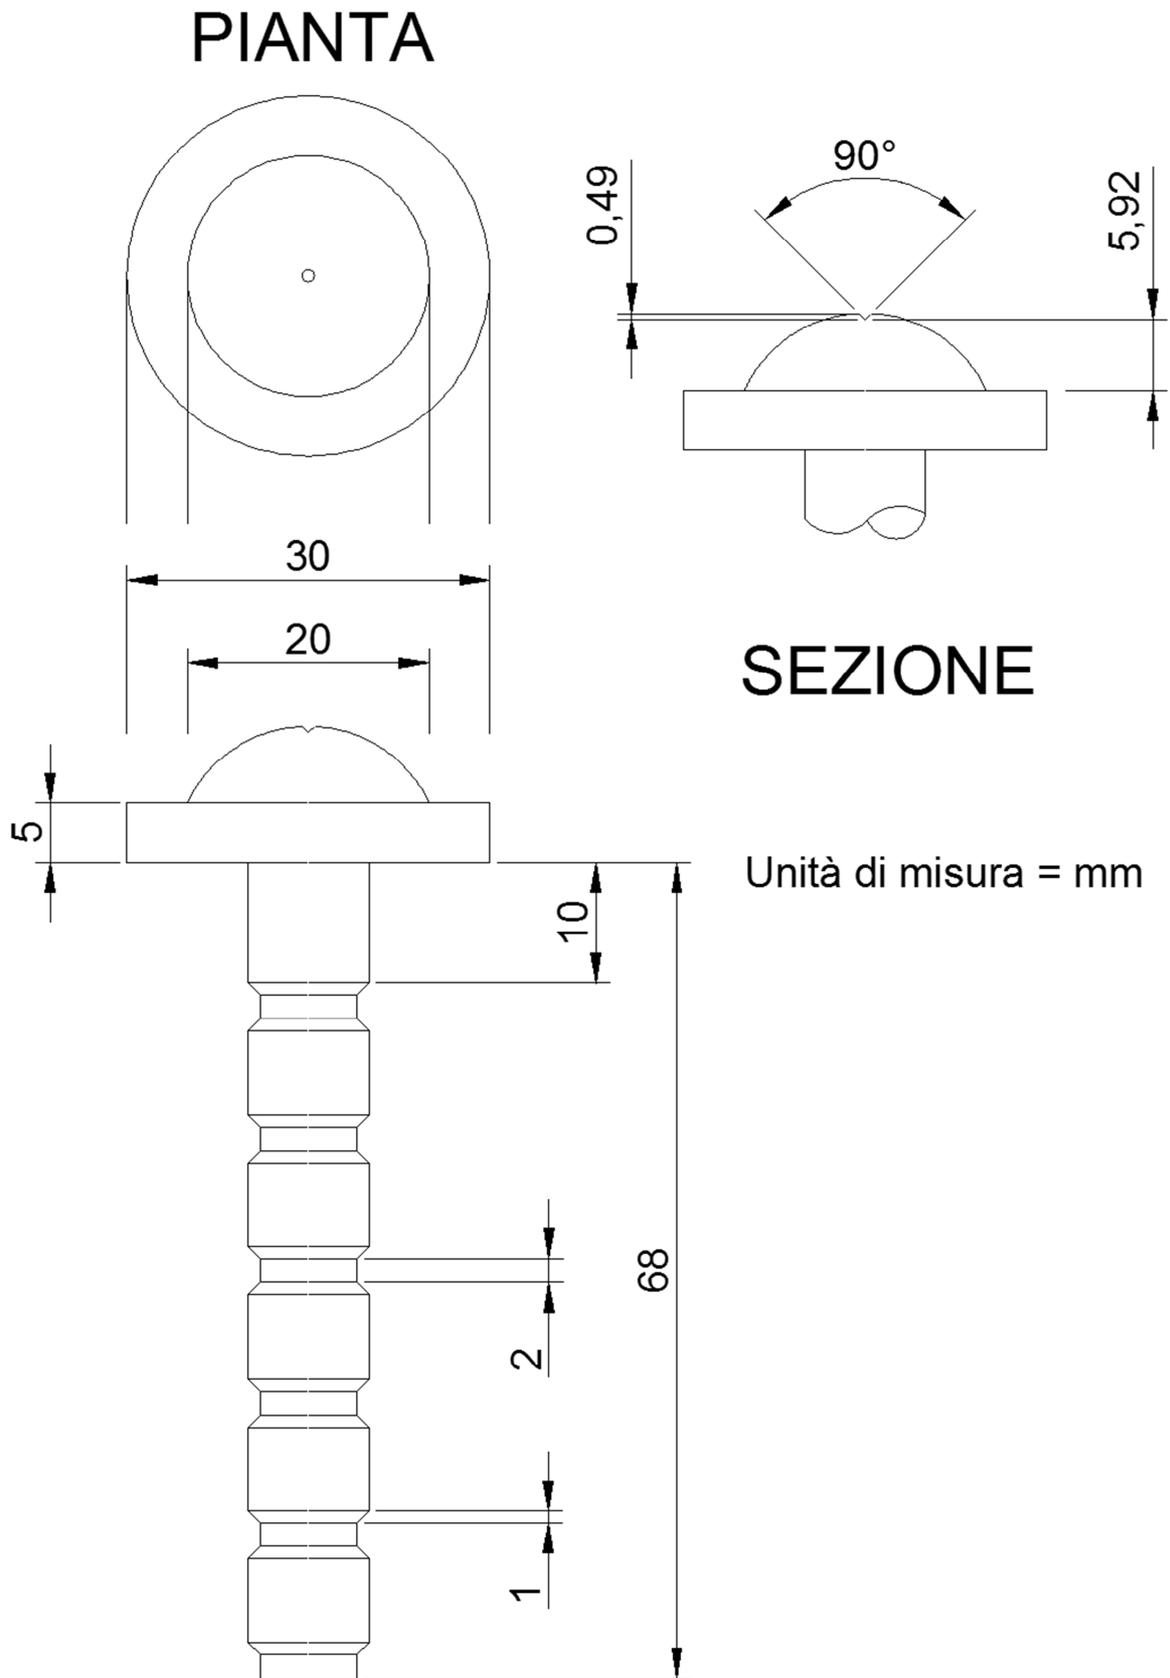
Pianta e sezione tipo della corona/rondella del capisaldo (principale e secondario) e del pilastro di sezione
